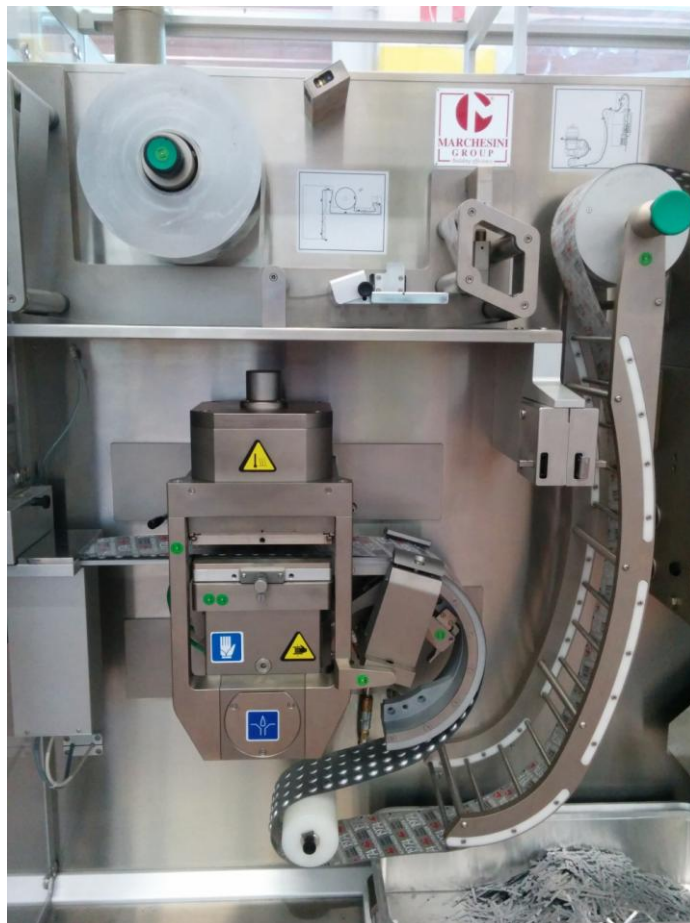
Gruppo Centratrice Stampa e Saldatura
